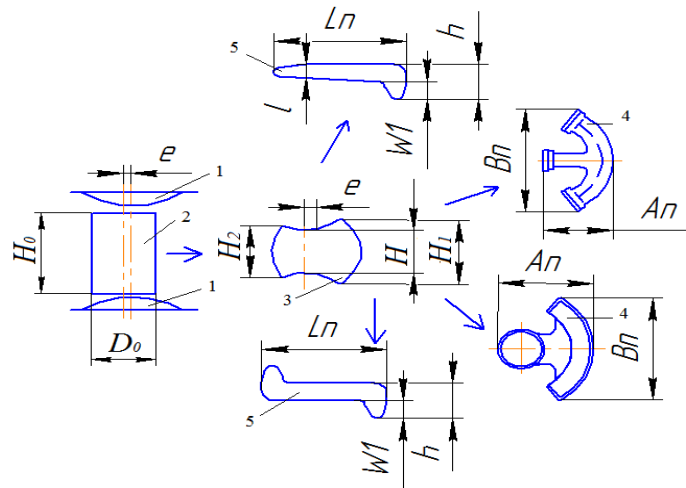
Варианты штамповки поковок с предварительным профилированием заготовки осадкой выпуклыми продолговатыми плитами с эксцентриситетом: 1 – осадочные плиты с радиусом выпуклости  $R$ ; 2 – исходная заготовка; 3 – профилированная заготовка (размеры  $H$ ,  $H_1$  и  $H_2$ ); 4 – поковка без облоя (габариты  $A_n$  и  $B_n$ ); 5 – пластина с отрезками;  $e$  – эксцентриситет оси плит и оси заготовки
